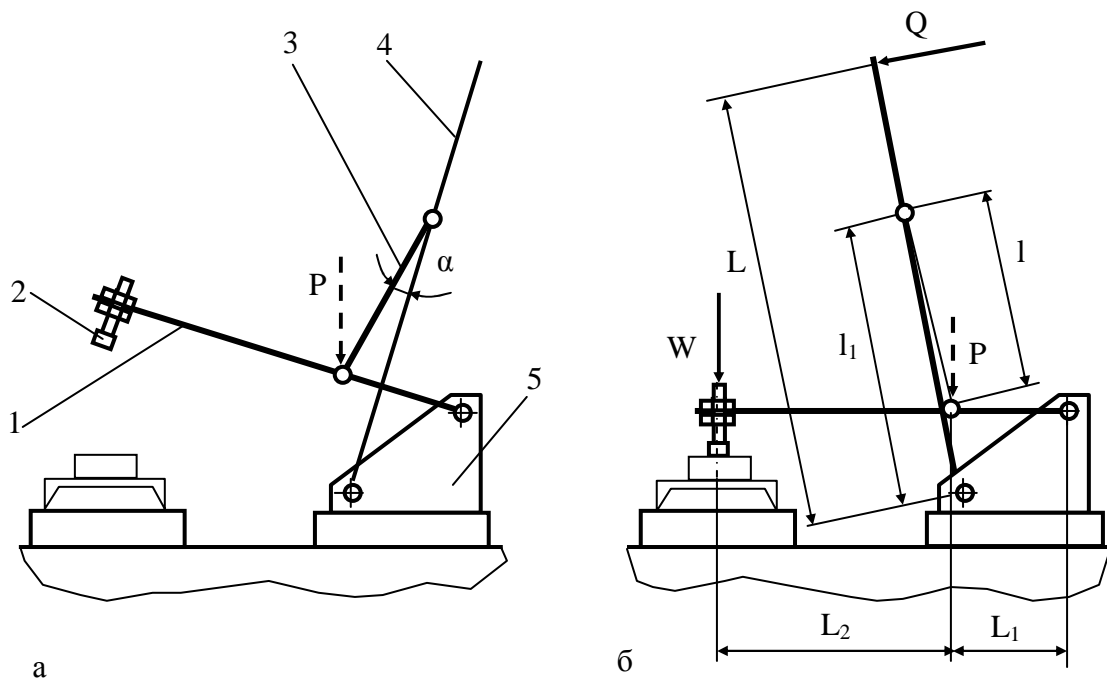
Схема ручного важільно-шарнірного притискача:
